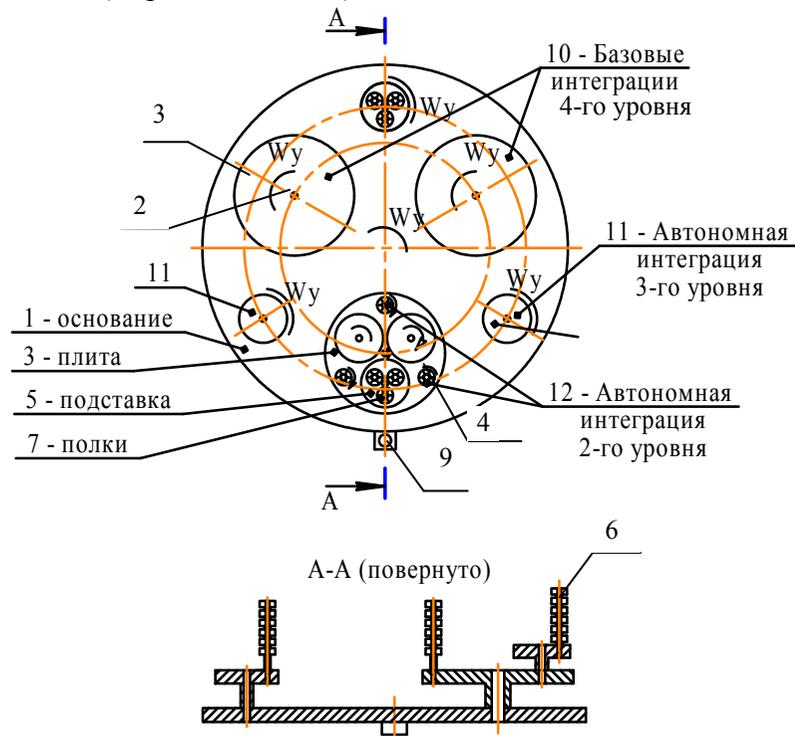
Механизированный склад 356206, МКИ В65 G/02
